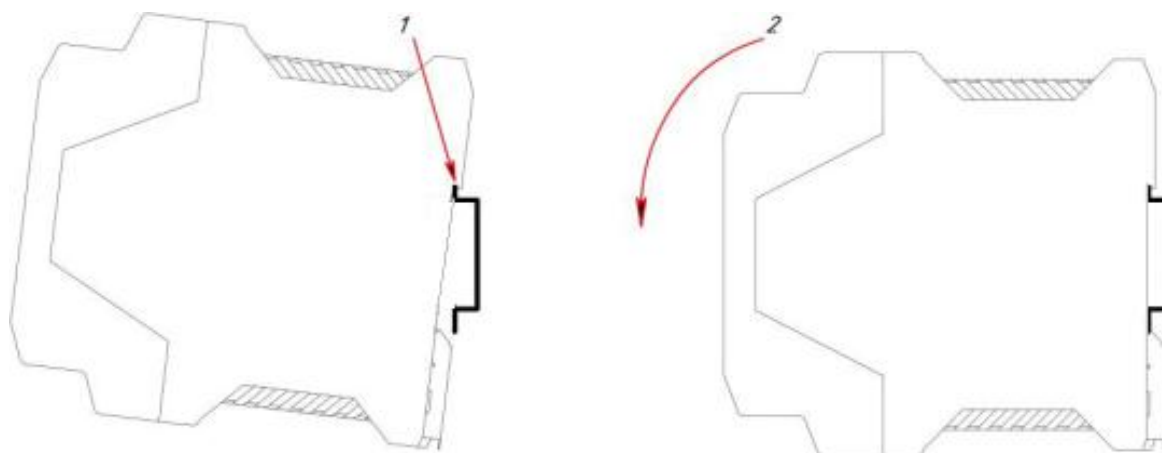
Схема крепления преобразователя ПНС-101 на DIN-рельсе
